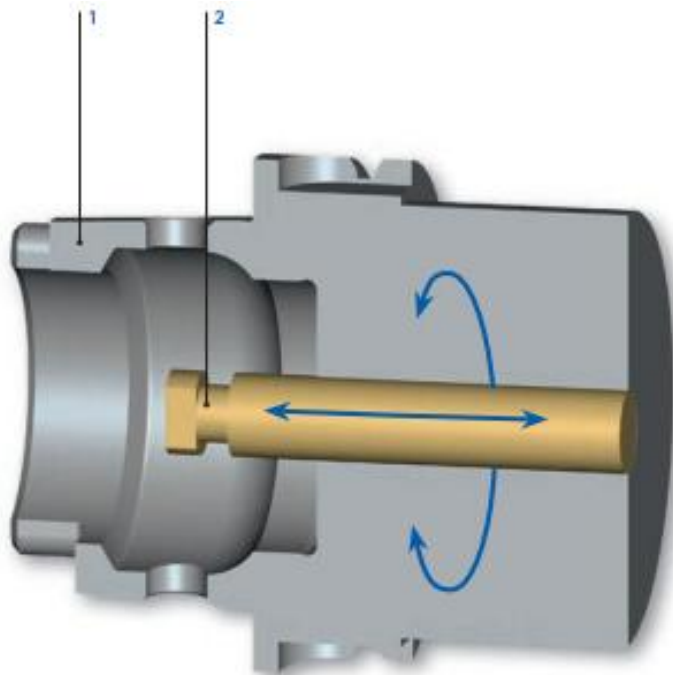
Конструкція виходу супорта через вісь U верстата [4]:
